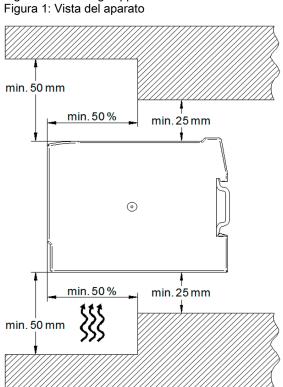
Einbau Figure 2: Installation Figure 2: Montage
